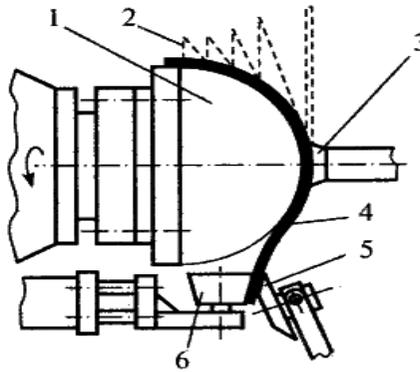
Схема ротационной вытяжки полусферы: 1 – оправка; 2 – последовательность процесса; 3 – прижимная бабка; 4 – заготовка; 5 – давящий ролик; 6 – поддерживающие ролики
